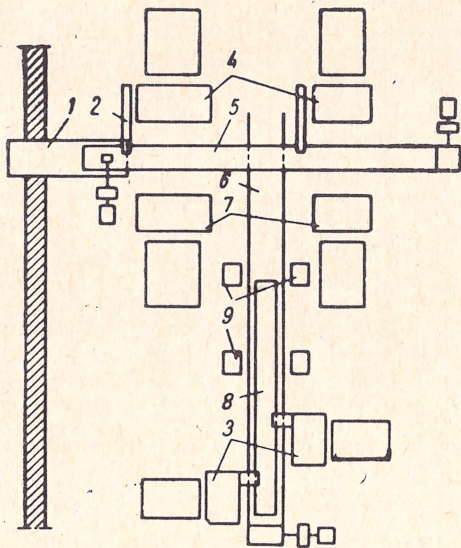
Схема механизированной уборки стружки в токарном отделении
